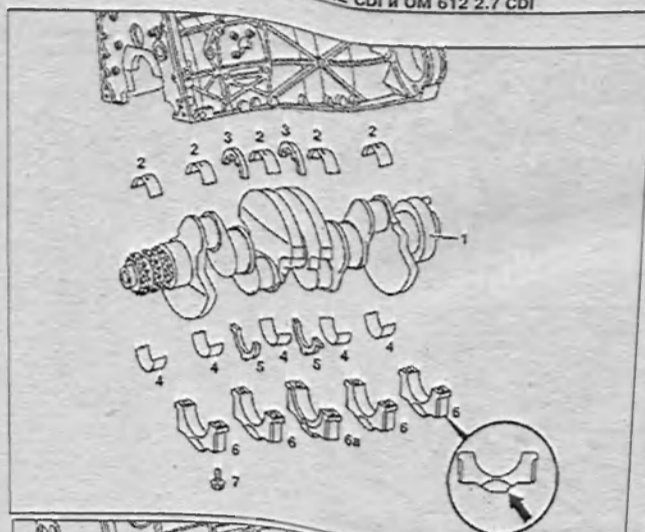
а. Коленчатый вал двигателей OM 611:
